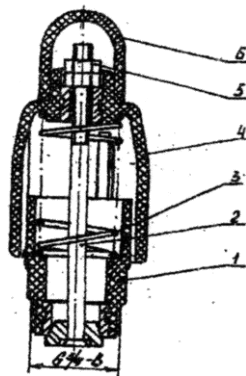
Вакуумний регулятор доїльної устатковини для індивідуального доїння корів: 1 – корпус; 2 – клапан; 3 – пружина; 4 – стакан; 5 – гайка; 6 – ковпачок
